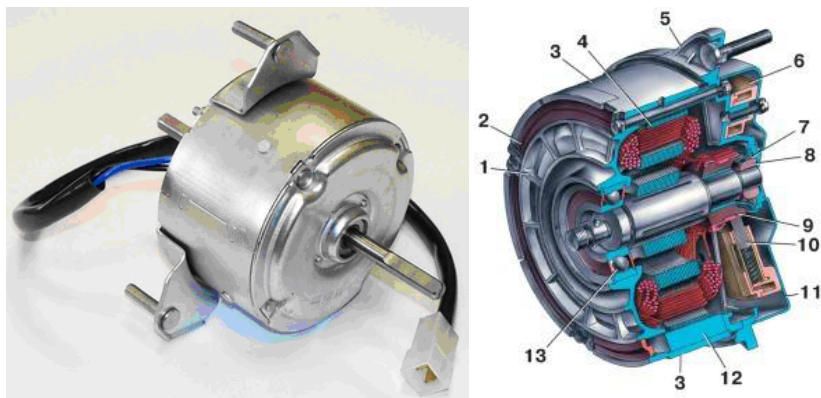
Внешний вид (слева) и устройство (справа) электродвигателя вентилятора системы охлаждения двигателя МЭ-272: 1 – корпус электродвигателя; 2 – грязезащитное кольцо; 3 – держатель магнитов; 4 – якорь электродвигателя; 5 – крышка; 6 – щеткодержатель; 7 – войлочное кольцо; 8 – втулка; 9 – коллектор; 10 – щетка; 11 – кожух; 12 – магнит; 13 – шариковый подшипник
